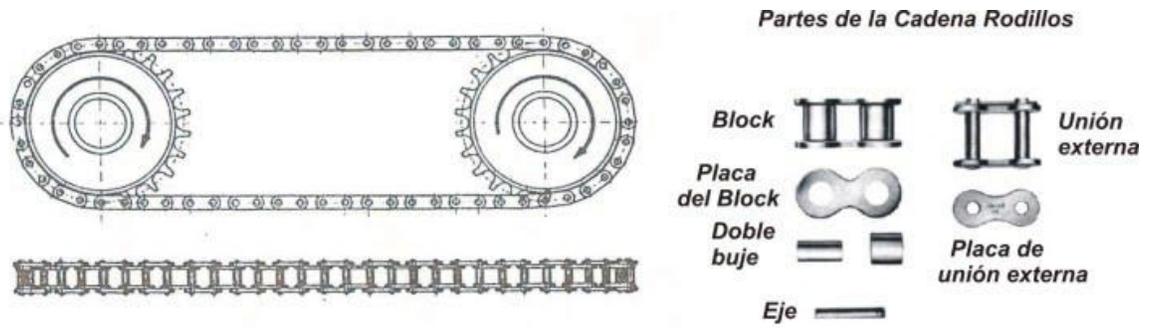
cadena de transmisión de movimiento mediante engranes.
